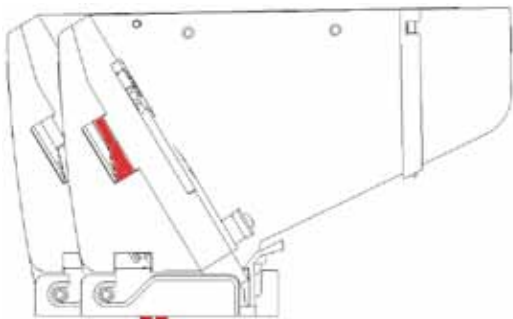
Montagehalterung mit großer Grundplatte installieren
